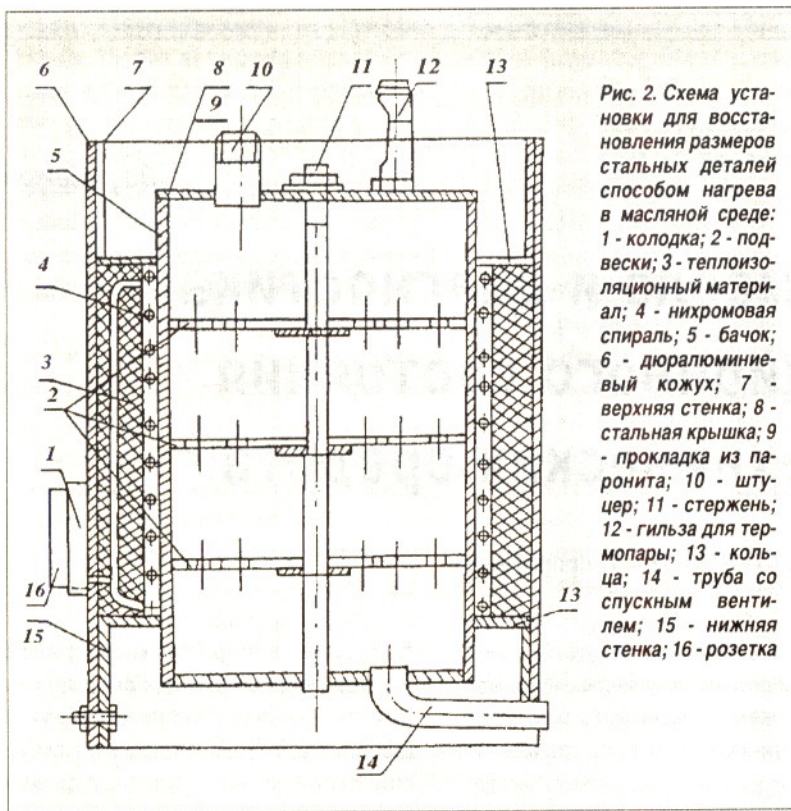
Схема установки для восстановления размеров стальных деталей способом нагрева в масляной среде: 1 - колодка; 2 - подвески; 3 - теплоизоляционный материал; 4 - нихромовая спираль; 5 - бачок; 6 - дюралюминиевый кожух; 7 - верхняя стенка; 8 - стальная крышка; 9 - прокладка из паронита; 10 - штуцер; 11 - стержень; 12 - гильза для термомпары; 13 - кольца; 14 - труба со спускным вентиляем; 15 - нижняя стенка; 16 - розетка
